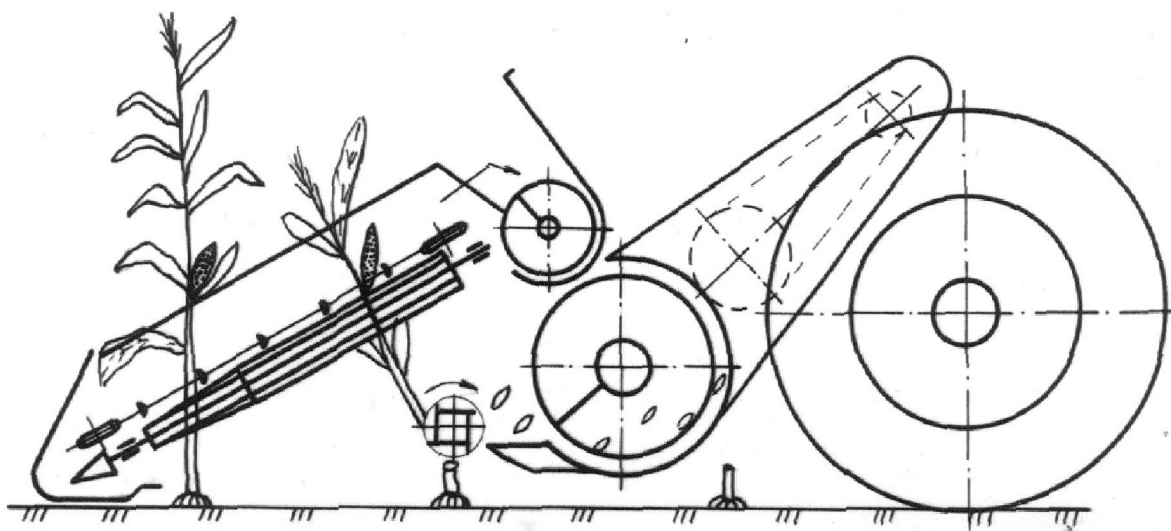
Схема приспособления с роторным режущим аппаратом
